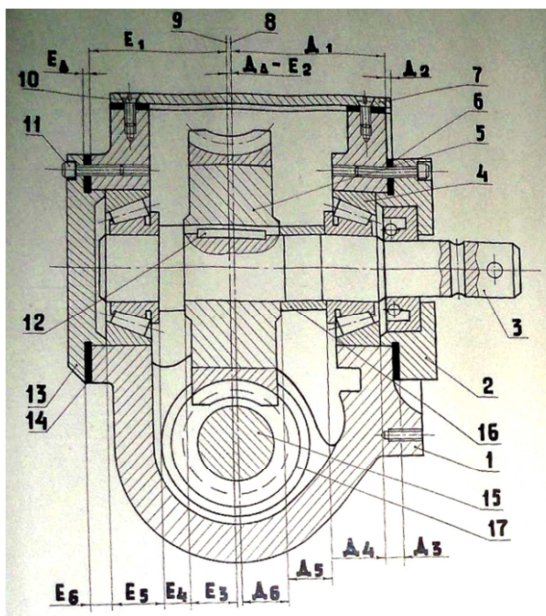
Конструкція системи «корпус – вал – червячне колесо» червячного редуктора з елементами розмірного ланцюга, що забезпечує складаність системи
